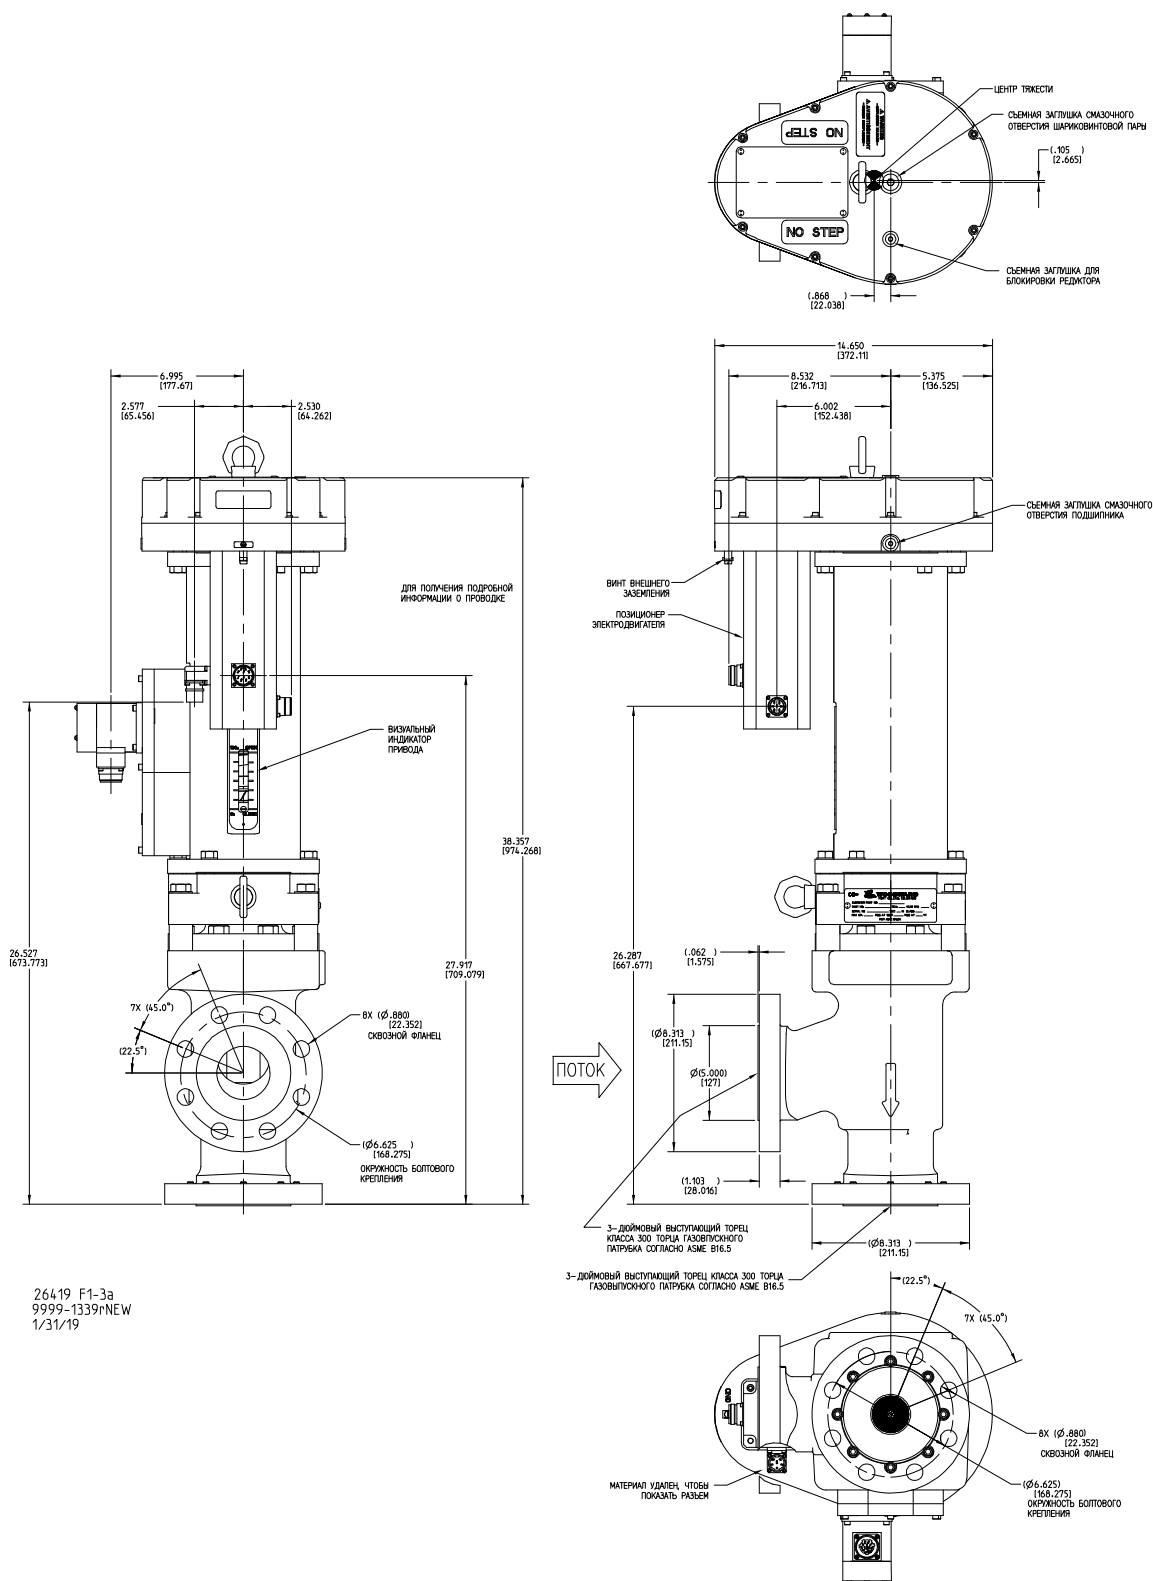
а. Габаритный чертеж (3-дюймовый клапан LESV класса 300)
